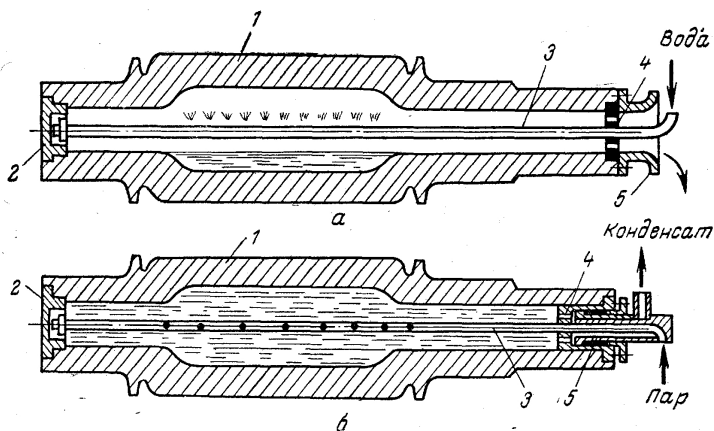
Валок каландра: а – охлаждаемый валок (1 – валок; 2 – заглушка; 3 – трубка подвода охлаждающей воды; 4 – опора; 5 – сливная воронка); б – обогреваемый валок (1 – валок; 2 – заглушка; 3 – труба подачи пара; 4 – уплотнение; 5 – канал для слива конденсата)
